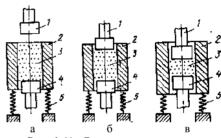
Схема двустороннего прессования с подвижной («плавающей») пресс-формой: а - засыпная форма; б - начало перемещения формы при прессовании; в - конец прессования; 1 - верхний пуансон; 2 - подвижная пресс-форма; 3 - прессуемая масса; 4 - нижний пуансон; 5 - пружины, поддерживающие пресс-форму
